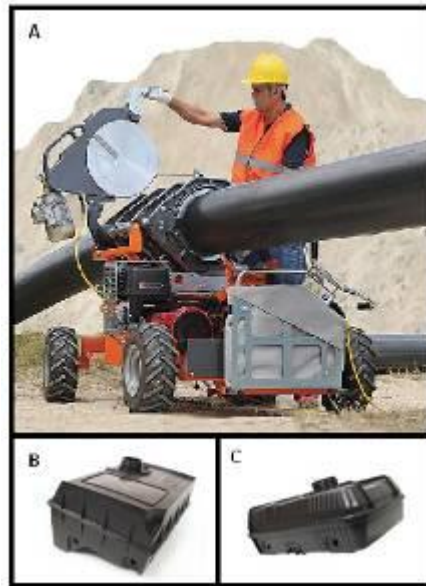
A) Soldadura de tuberías, B) y C) Soldadura en tanque de combustible.
